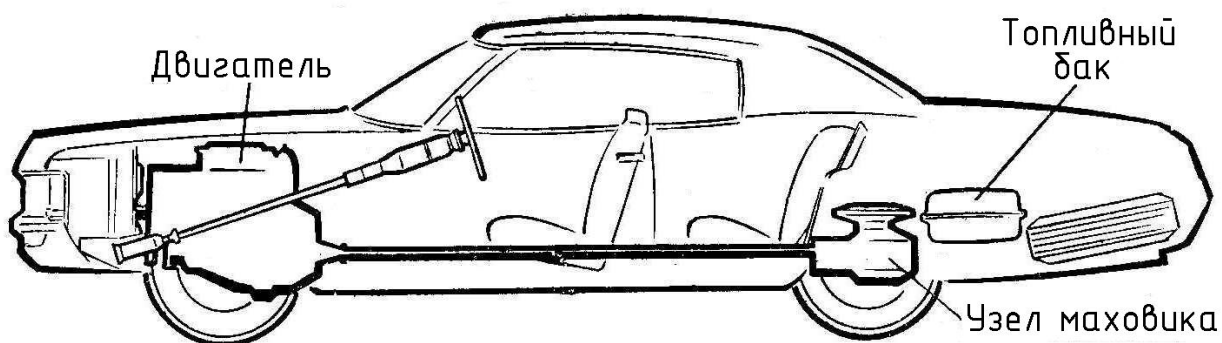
Компоновка гибридного силового агрегата с раздельным расположением двигателя и маховичного агрегата
